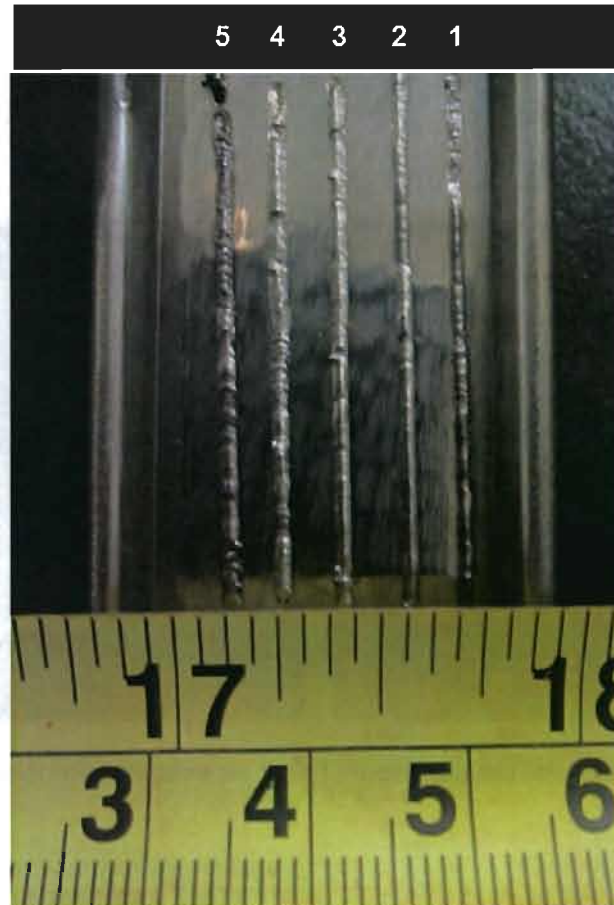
3 Inspección visual a cordones de soldadura
